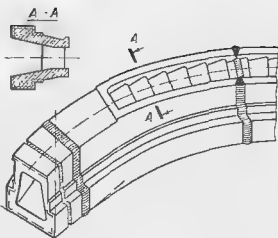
Сварно-литой сегмент сопла турбины
